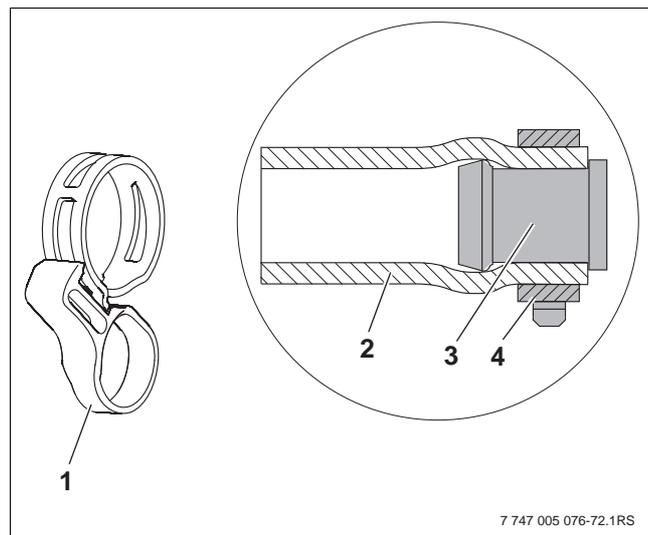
Abraçadeira de mola com anel de retenção e tampão cego pré-montado.
